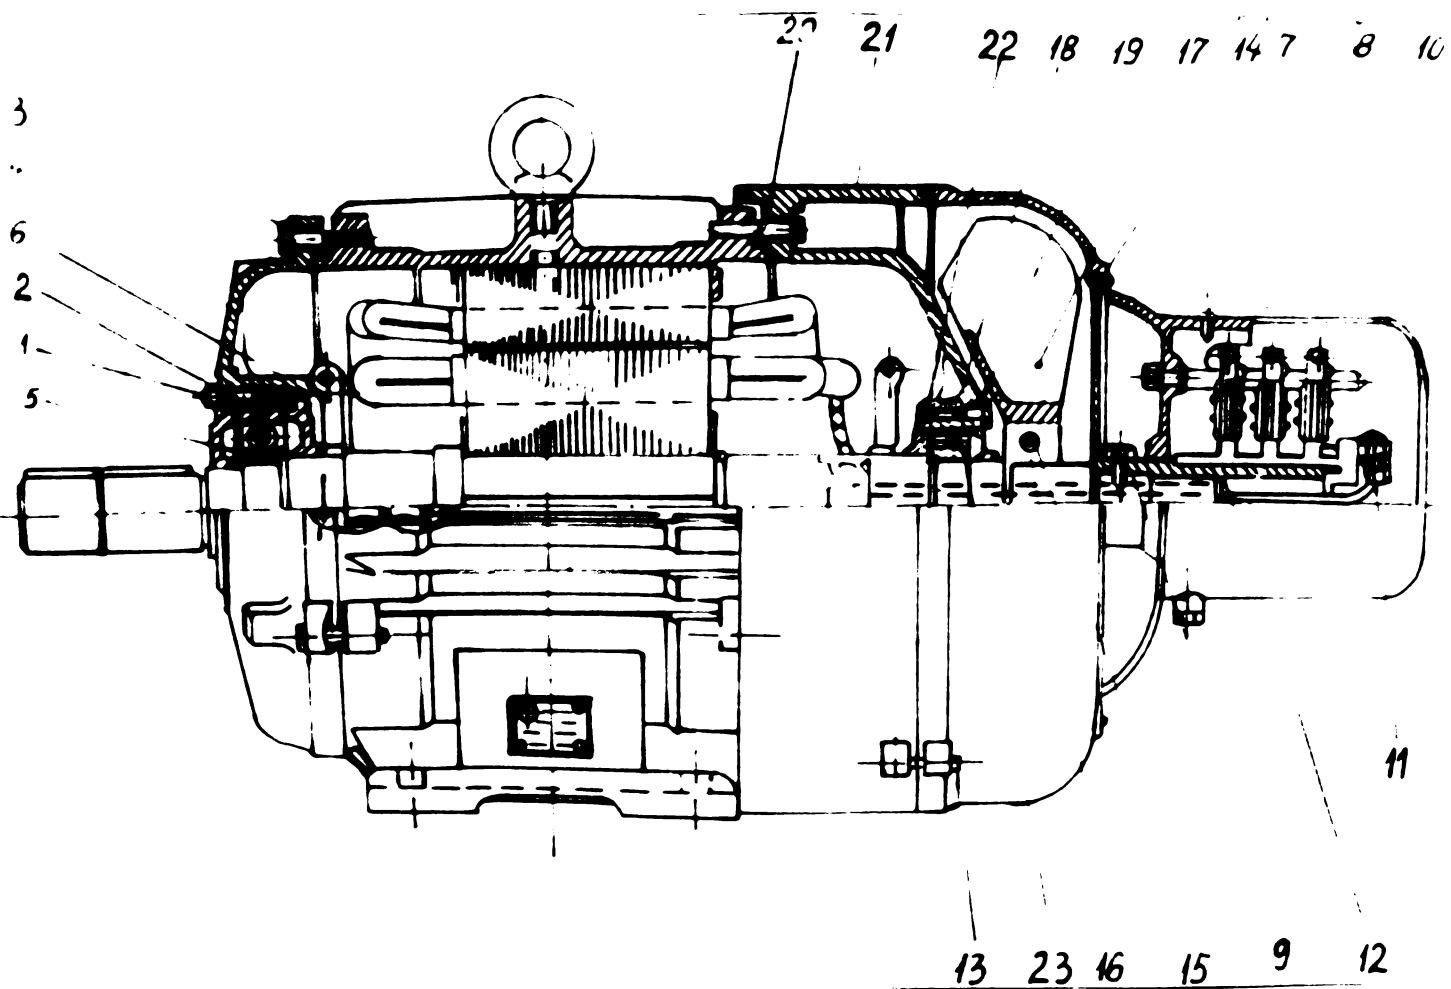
Motor electric asincron trifazat cu rotor bobinat.
